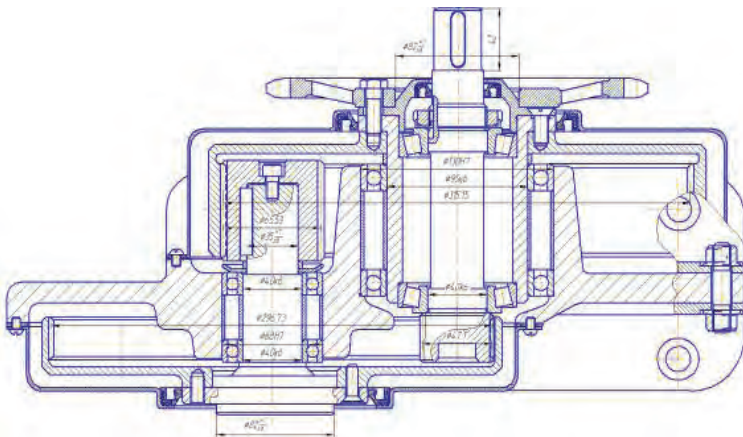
Соосный редуктор с внутренним расположением основной массы корпуса
